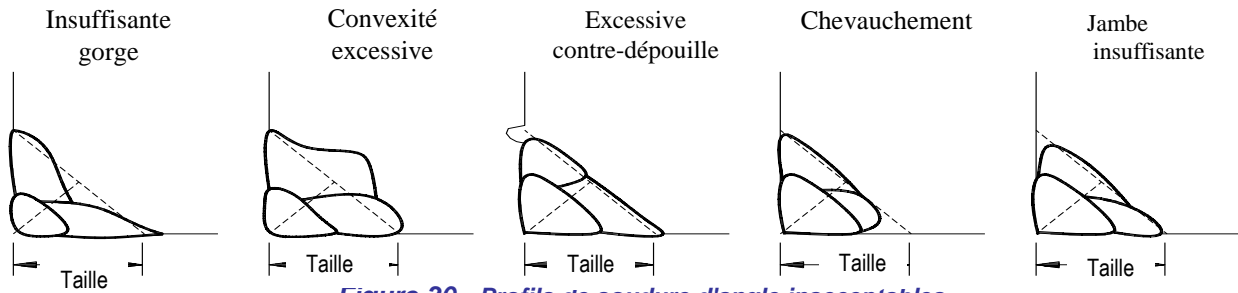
Profils de soudure d'angle inacceptables
